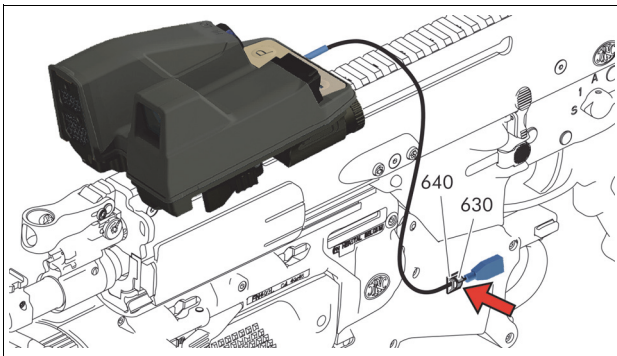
h - Guidage du câble de commande sur fusil, tireur gaucher
